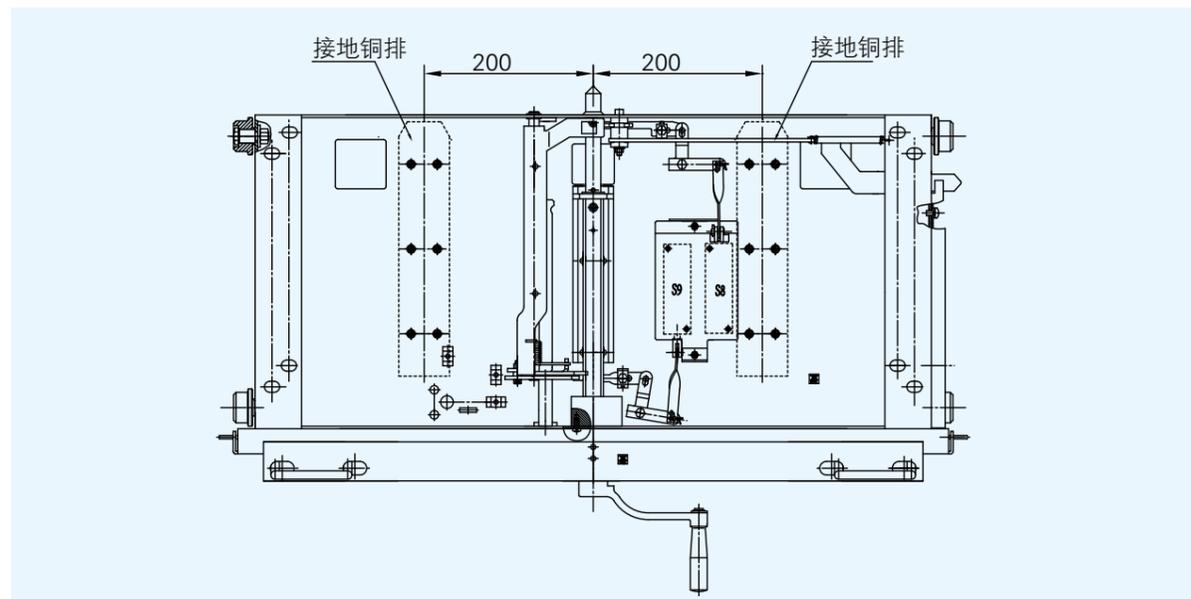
DPC-4-1000 接地铜排位置尺寸图
